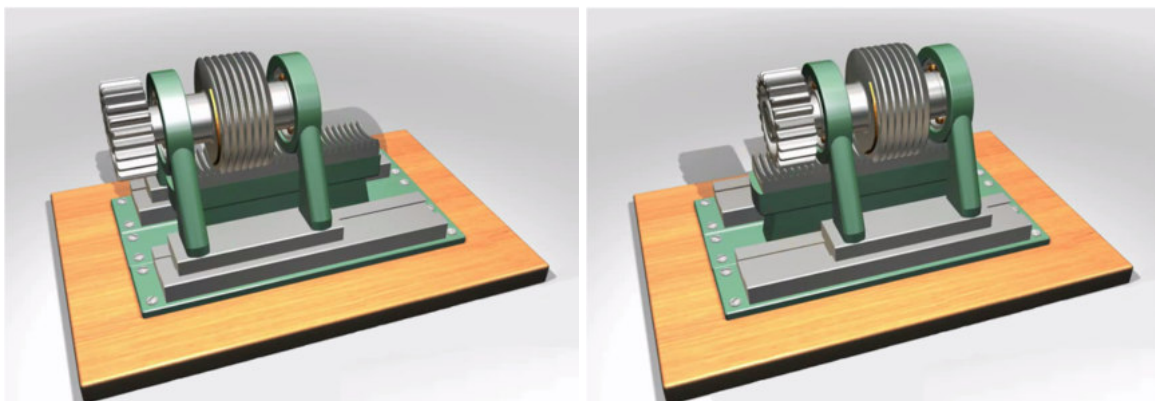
3D-модель черв'ячно-рейкової передачі (рейка не рухома)
